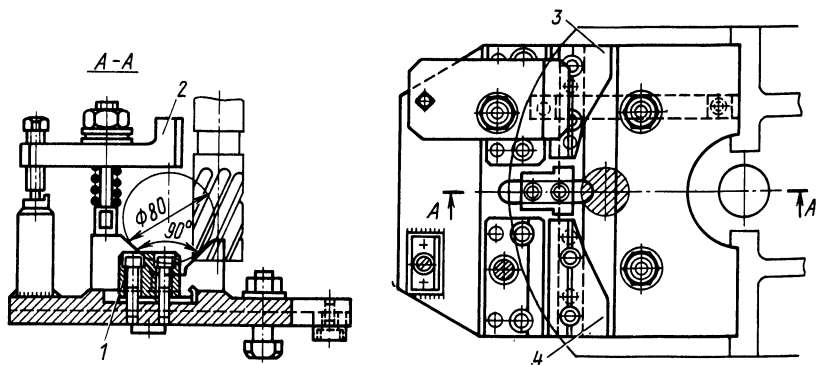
Приспособление для фрезерования радиусных поверхностей на валиках и втулках
